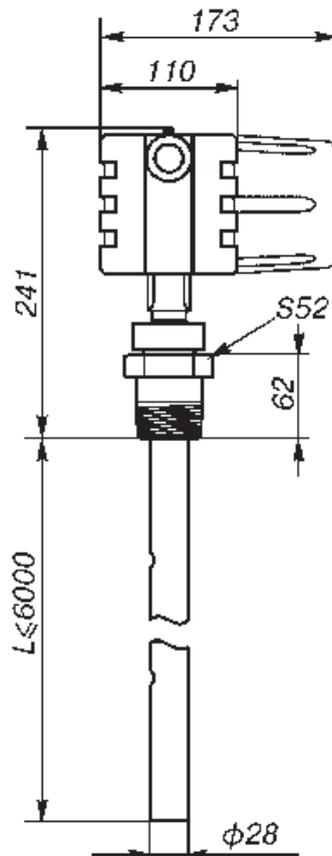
Габаритные и присоединительные размеры Rosemount 3300
